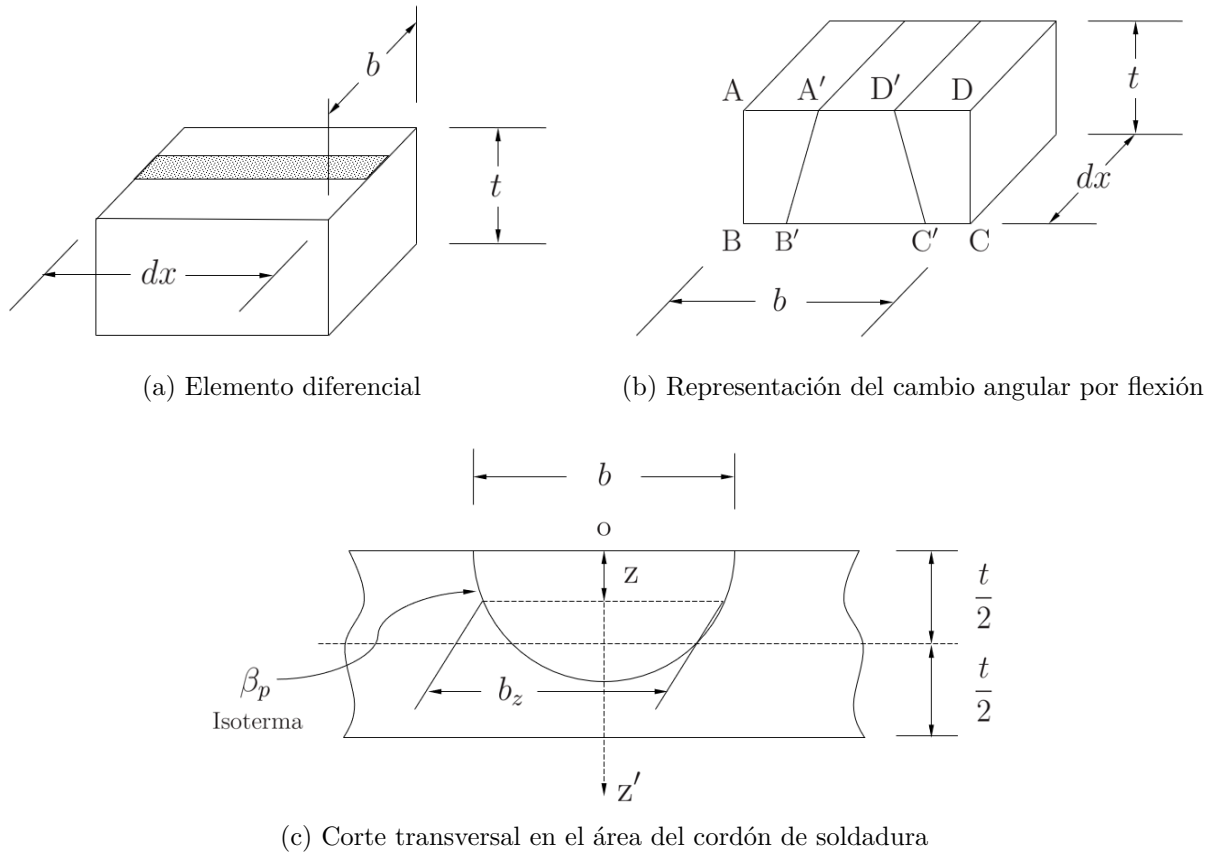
Elemento diferencial y corte transversal en la zona que rodea el cordón en una soldadura tipo *bead on plate*. [7]
